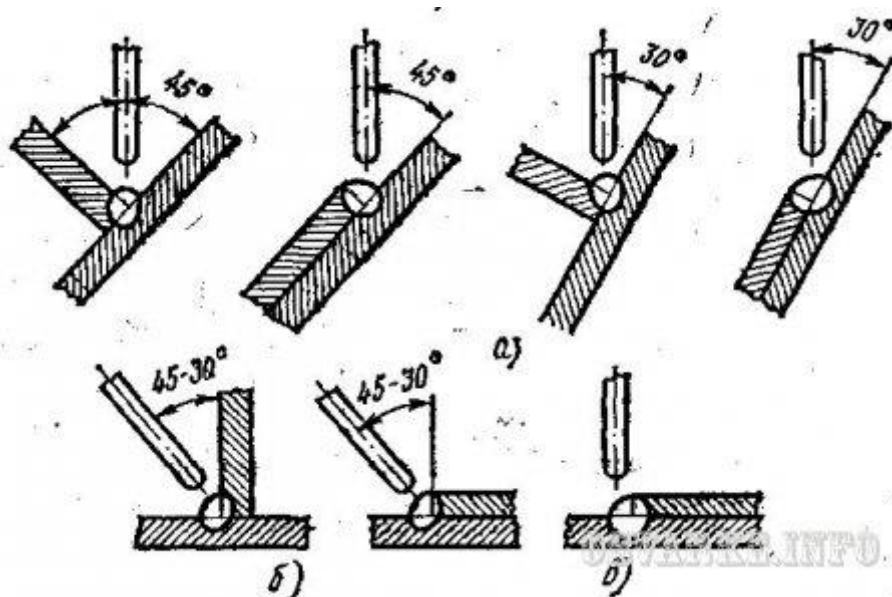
Способы выполнения угловых, тавровых и нахлесточных соединений: а - сварка в симметричную и несимметричную «лодочку», б - сварка наклонным электродом, в - сварка с оплавлением кромки
